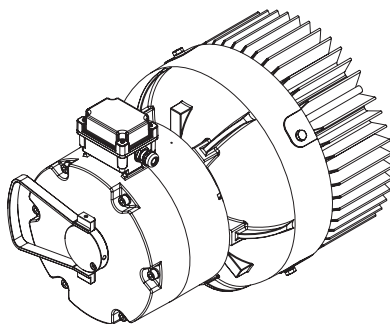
rem – types E../Z..075 en Z..100 – met blokkeerbaar handloszetmechanisme.
